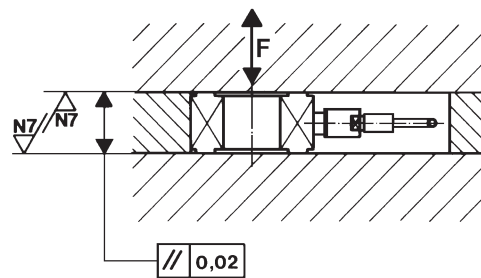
Einbau für Kraftnebenschlussmessung, Einlegen einer Stahlfolie auf die Messfläche des Sensors
